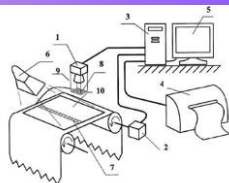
Схема устройства для обнаружения дефектов на движущейся ткани [3]
